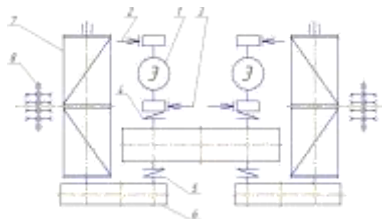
Конструкция с «тройным» редуктором (схема №7)
